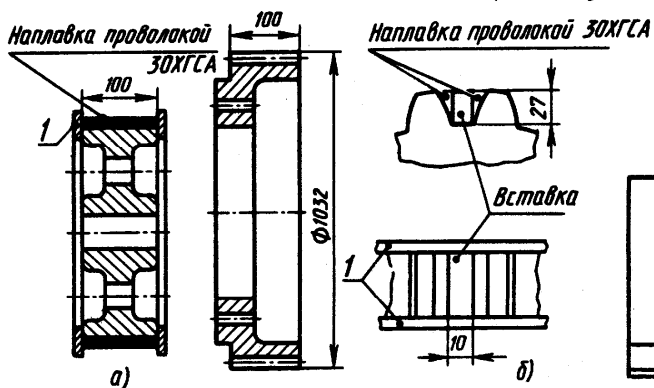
Схема наплавки зубчатых колес: 1-ограничительные планки
